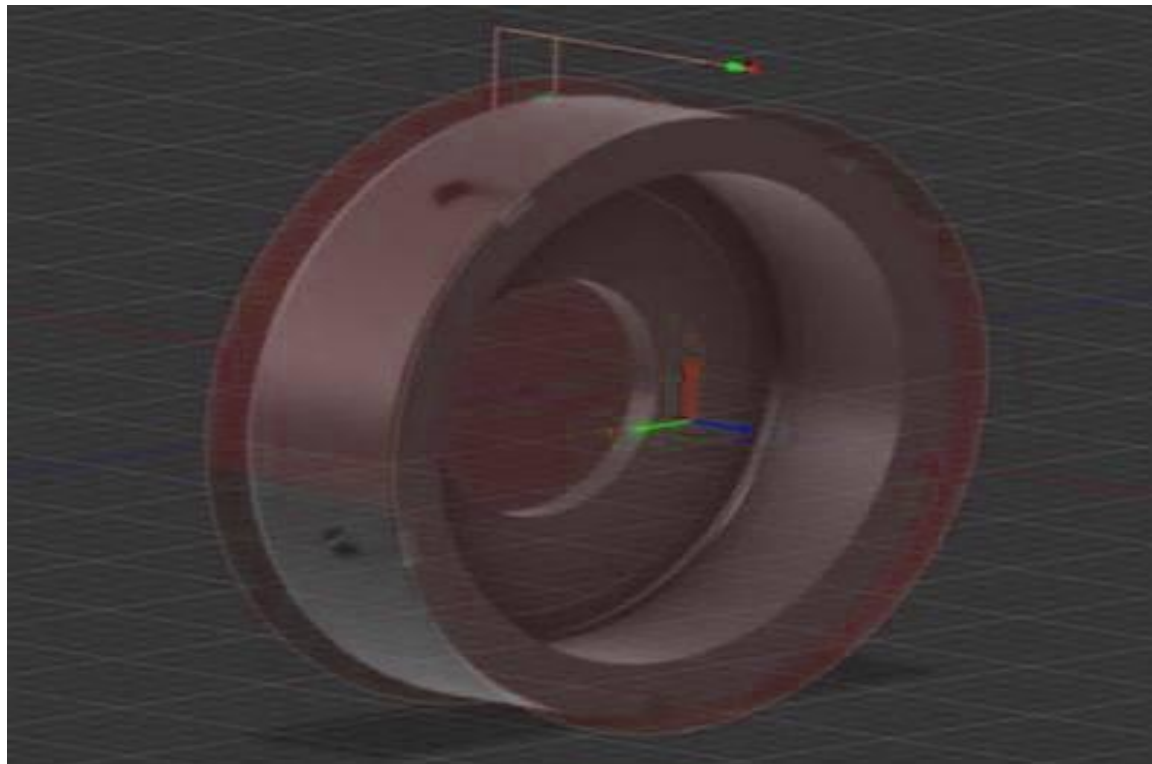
Сірим кольором позначені наша передня зовнішня кришка, червоним заготовка, з якої буду виготовляти.
